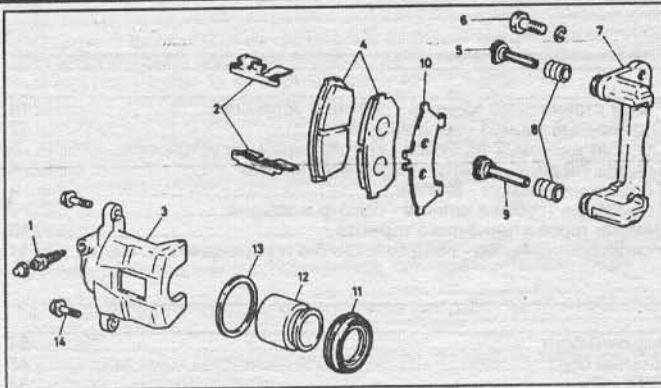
а Сборка переднего тормоза фирмы Tokico: 1 - штуцер прокачки; 2 - фиксатор колодок; 3 - суппорт; 4 - колодки; 5 - направляющий палец; 6 - болт направляющей; 7 - направляющая колодок; 8 - пыльник; 9 - направляющий палец; 10 - толкатель колодки; 11 - пыльник; 12 - поршень; 13 - уплотнение поршня; 14 - болт суппорта.
